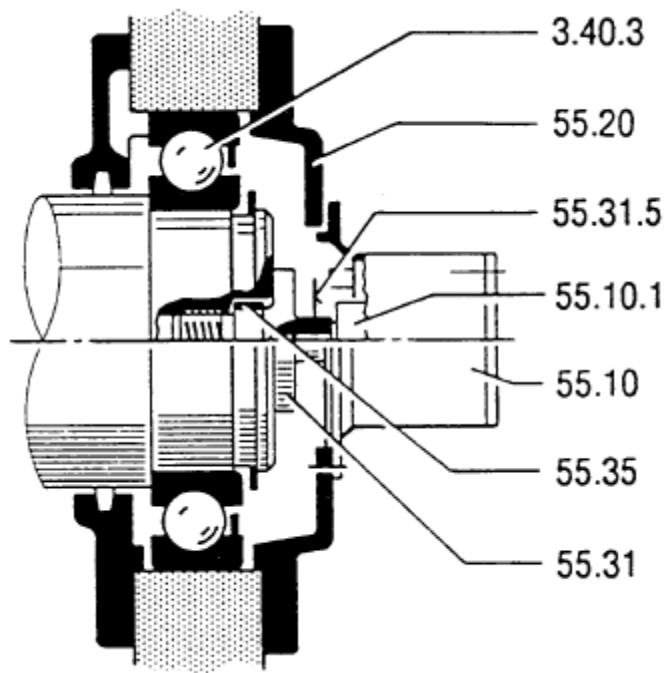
Transmissor de rotações para montagem suspensa para alturas de eixo de 180 a 630
